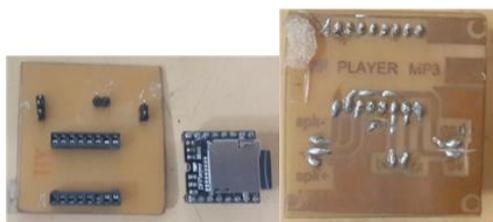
Placa del sistema de audio vista frontal y pistas soldadas vista posterior
